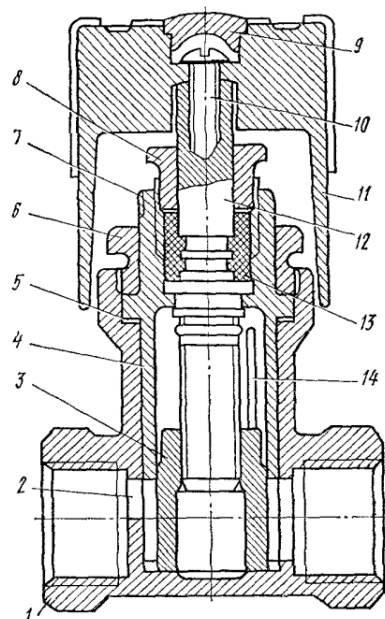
Кран двойной регулировки шиберного типа: 1 – корпус; 2 – регулировочное окно; 3 – шибер; 4 – поворотная втулка; 5 – прокладка; 6 – закрепительная гайка; 7 – риска на втулке; 8 – гайка сальника; 9 – крышка; 10 – винт; 11 – ручка; 12 – резьбовой шпindel; 13 – сальниковое уплотнение; 14 – паз во втулке
